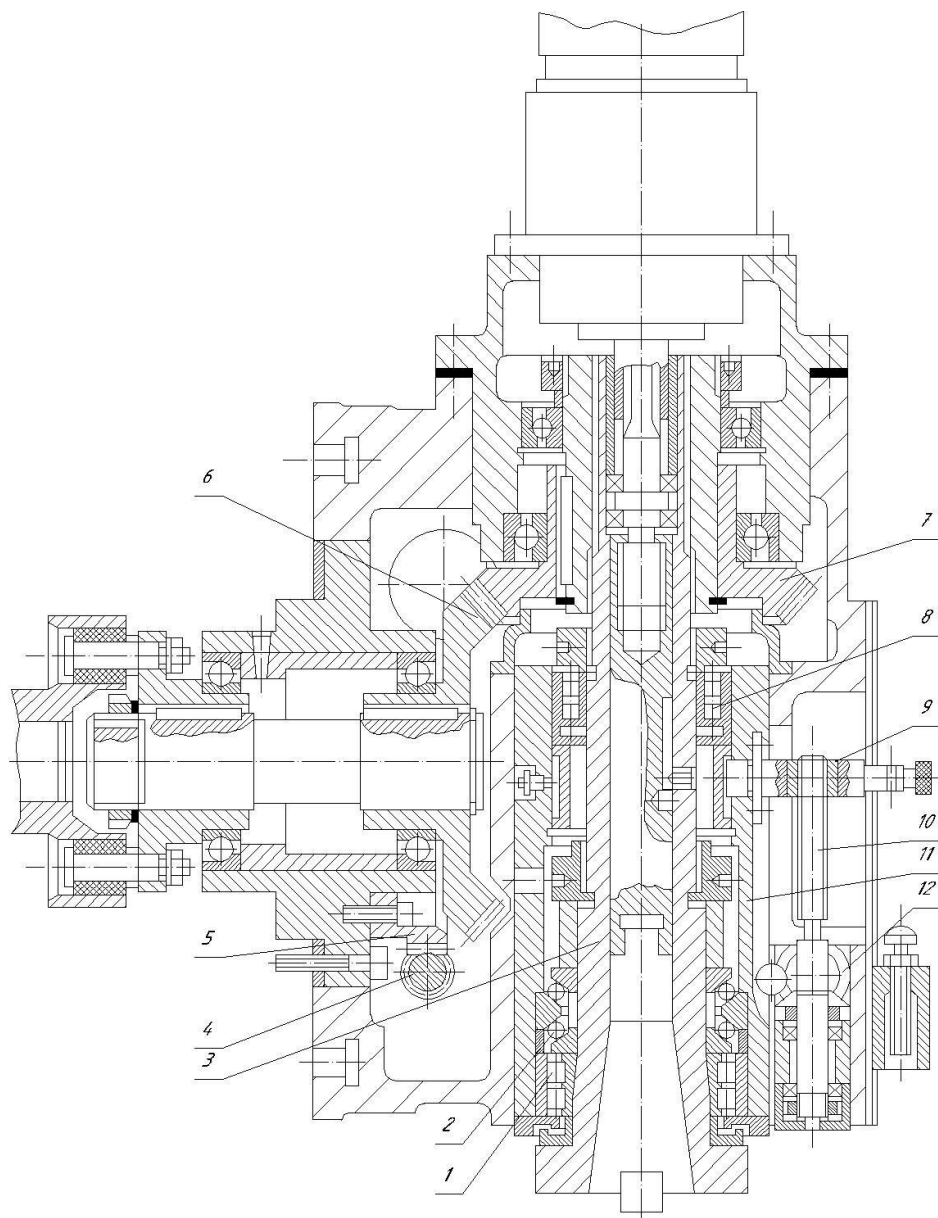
Фрезерная головка вертикального консольно-фрезерного станка.
